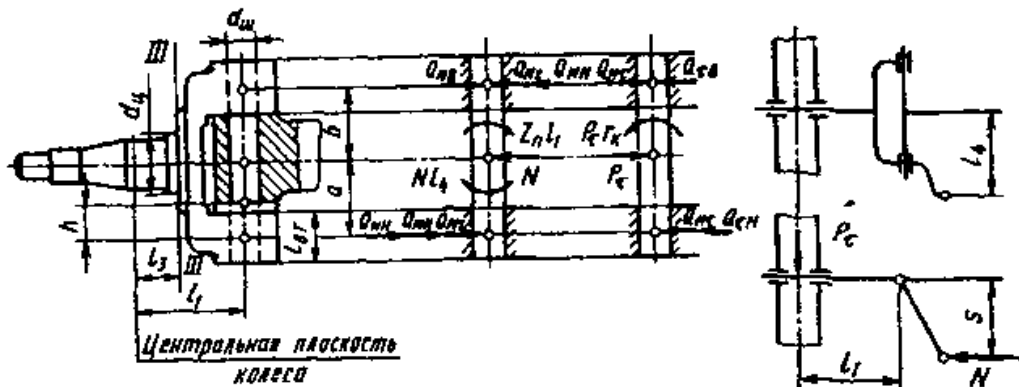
Розрахункова схема поворотного кулака, шворня і втулок
